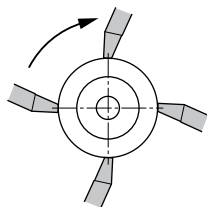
Перевірка осевого центрування за допомогою штангенциркуля — перевірка кола
